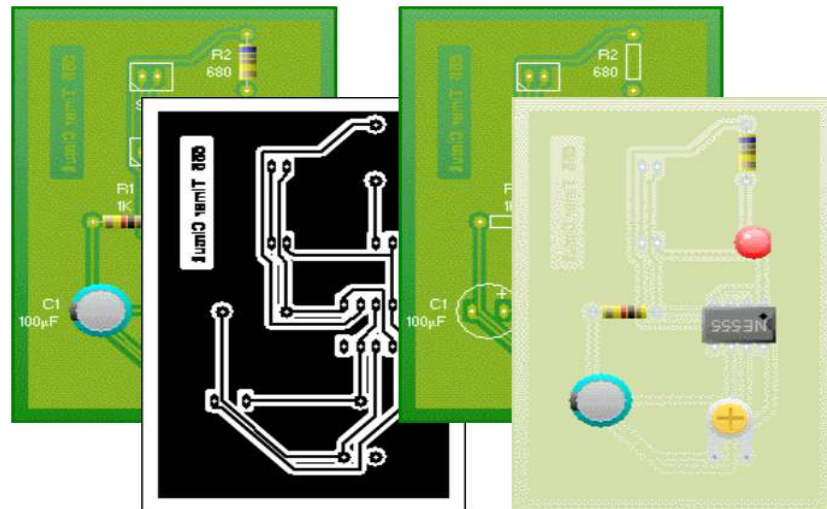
Distintas capas de diseño electrónico en Livewire y pcb wizard.
